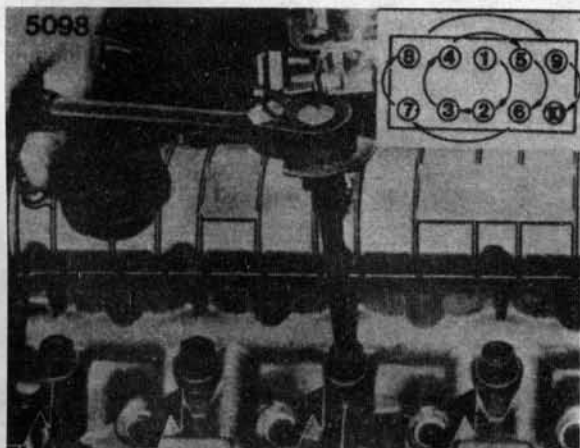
Очередность затягивания болтов головки блока цилиндров двигателя В172
